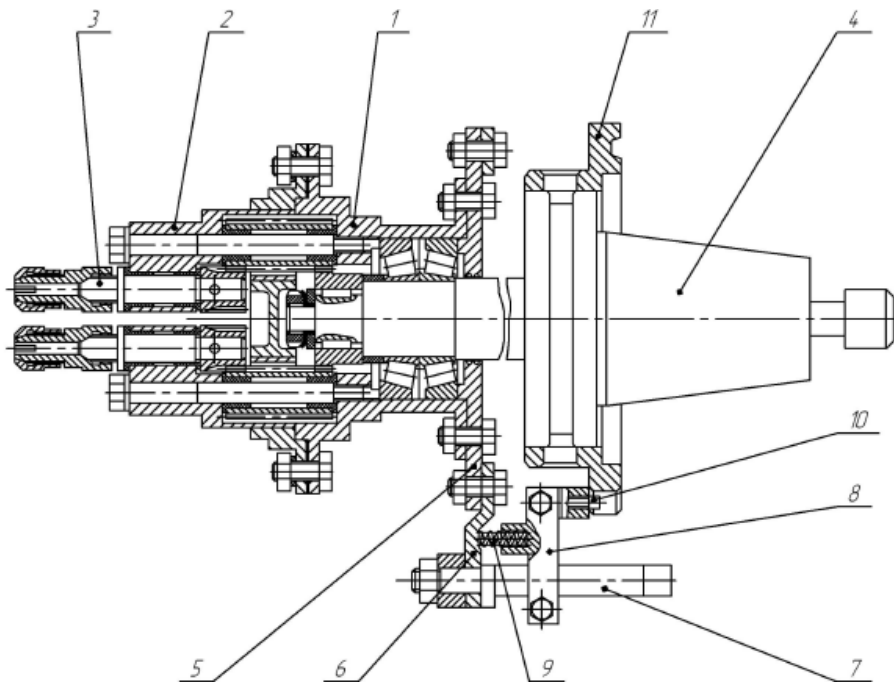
Багатошпindelна свердлильна головка для верстата зЧПК
